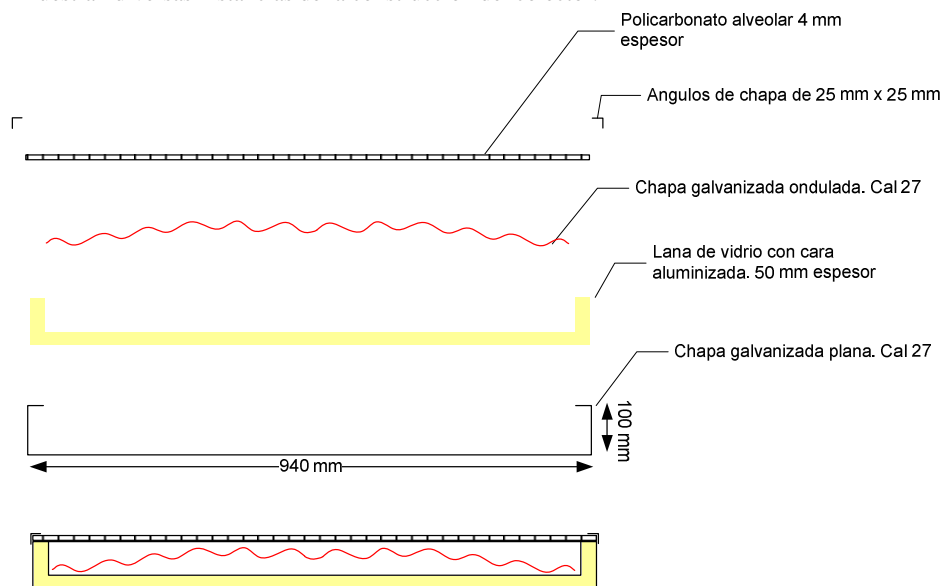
Esquema de sección transversal del colector. Se aprecian elementos constituyentes.
